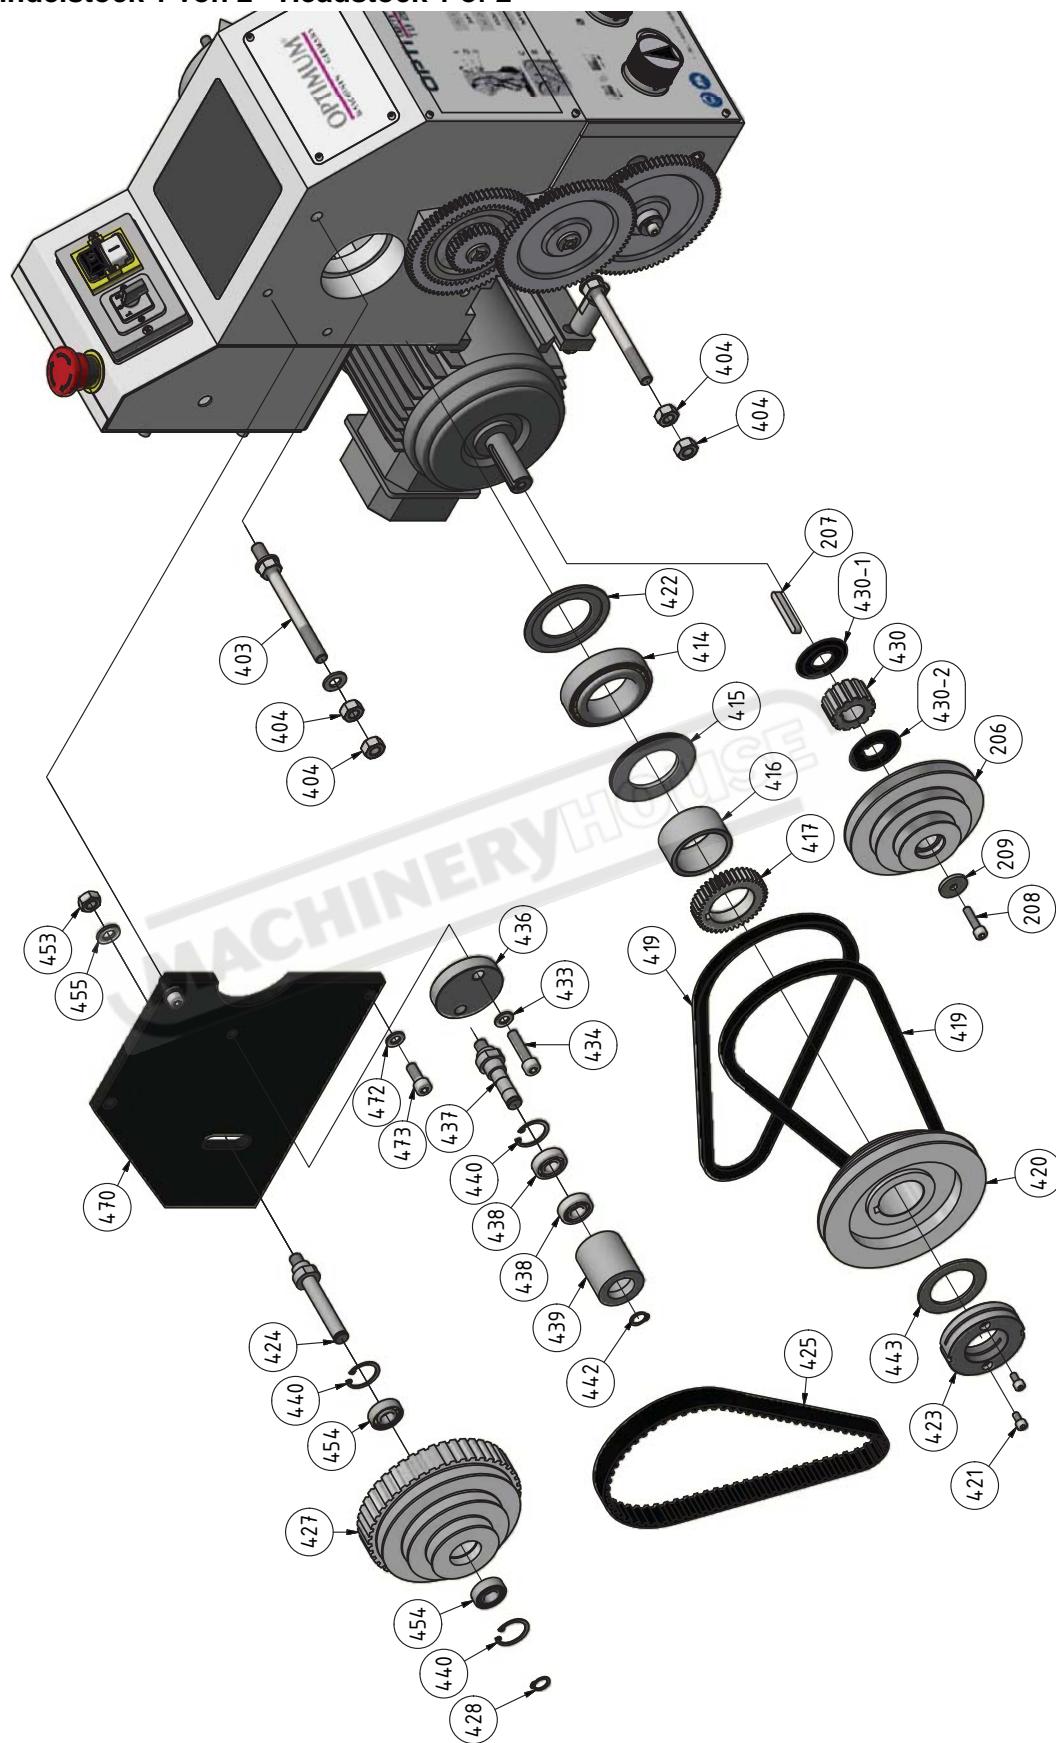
Spindelstock 1 von 2 - Headstock 1 of 2
